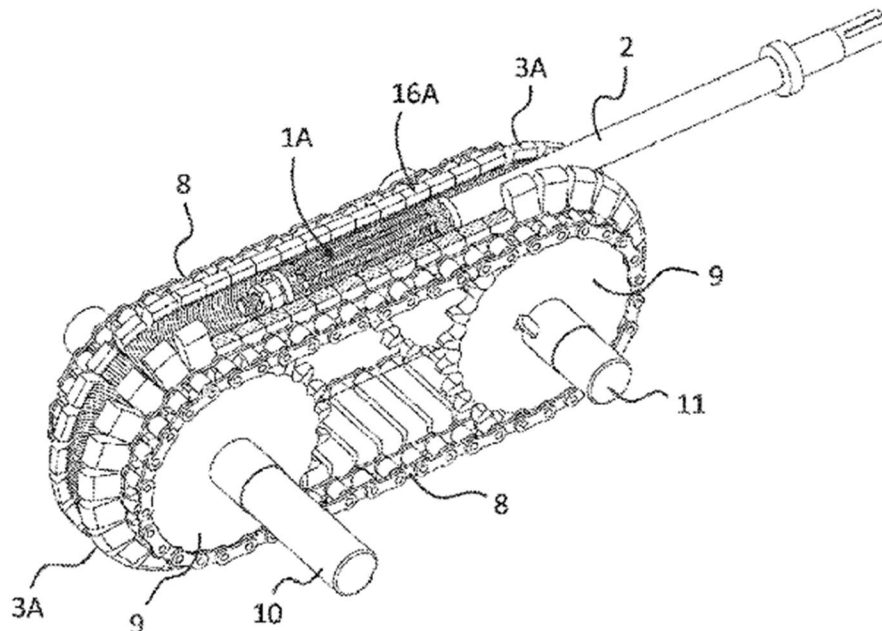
Esquema del ensamblaje del reductor integrando el tornillo de rodillos, (RVTICR-2) [5]
